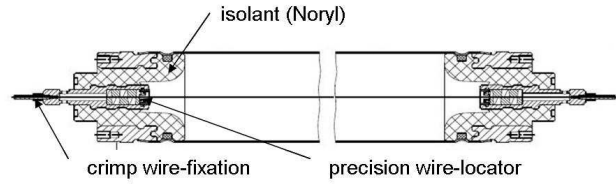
Vue en coupe longitudinale d'un tube de chambre de précision MDT.
